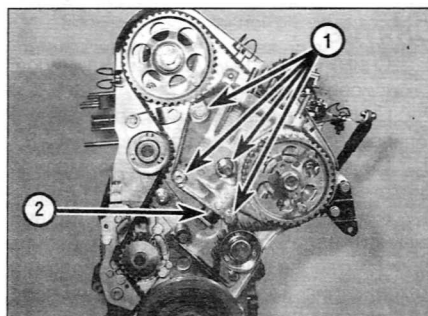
, а. Сторона двигателя, на которой расположен ремень газораспределительного механизма
